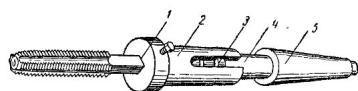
Приспособление для закрепления метчика при нарезании резьбы на токарном станке
